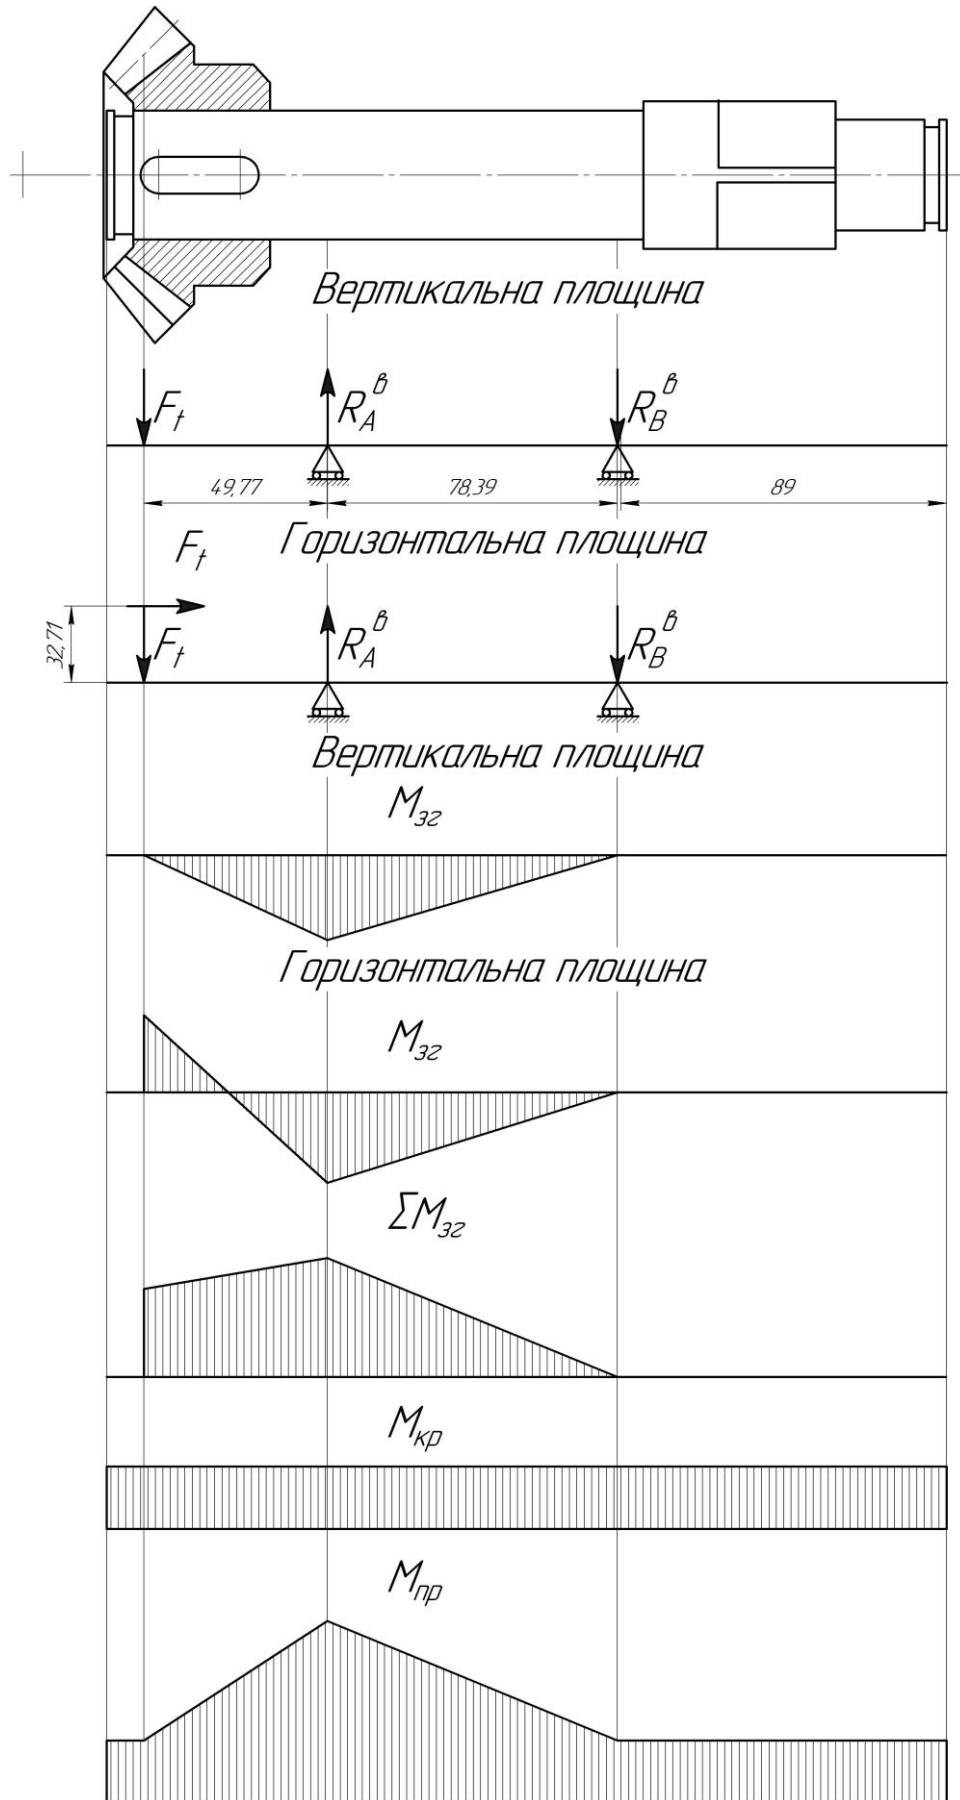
Схема сил, що діють на вихідний вал кутового редуктора
